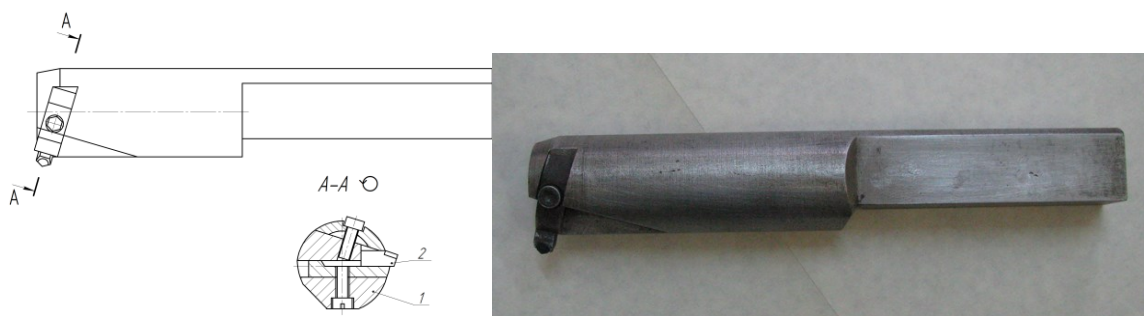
Конструкция и общий вид расточного резца с механическим креплением универсальной резцовой вставки: 1 – державка; 2 – резцовая вставка
